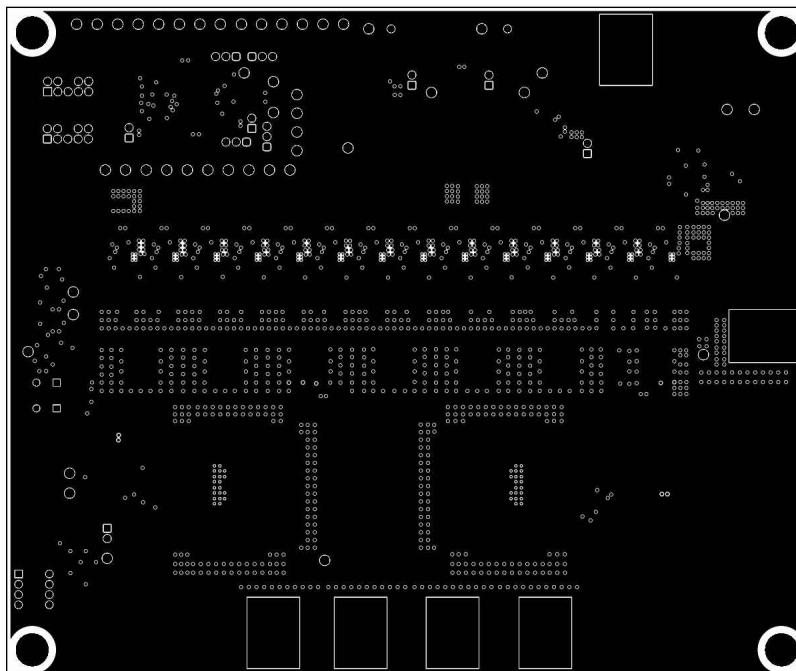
TPS53676EVM-084 PCB 第 9 层 - GND
